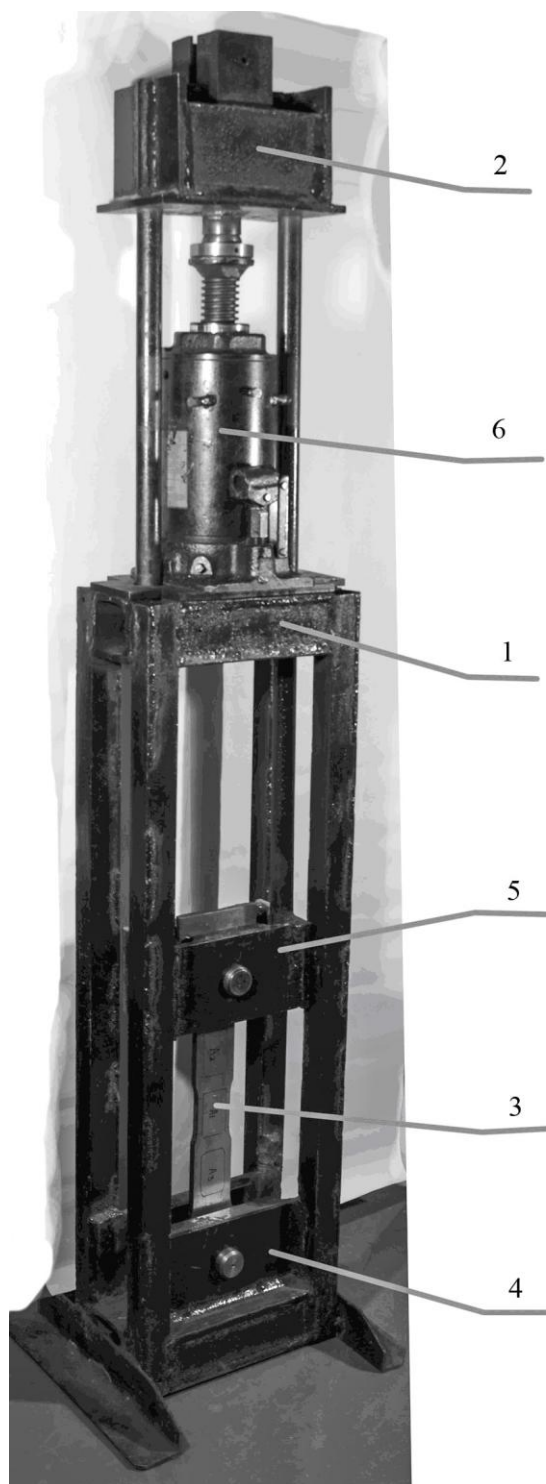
Загальний вигляд машини для пластичного деформування. 1- корпус, 2 - рухома частина, 3 – зразок, 4 – нерухомий захват, 5 – рухомий захват, 6 – ручний гідравлічний домкрат
